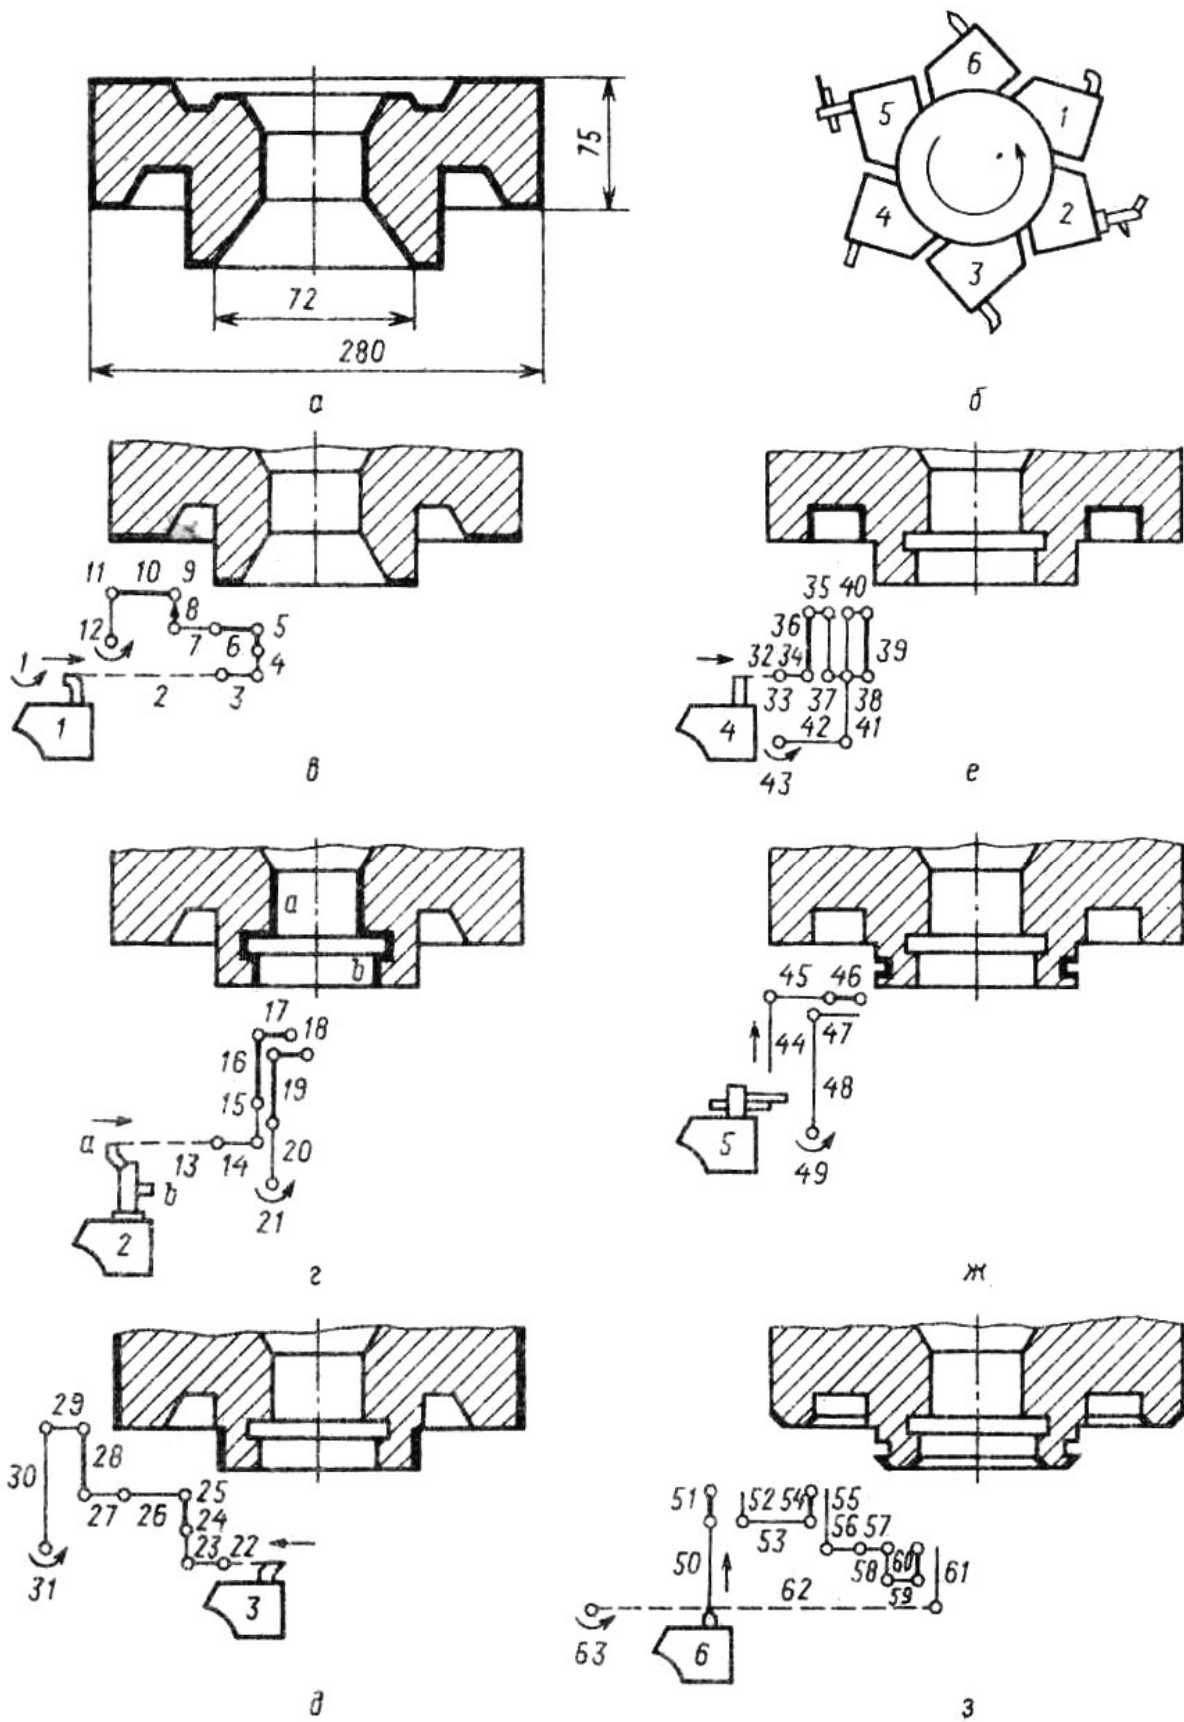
Многоинструментальная обработка на токарном станке с ЧПУ
